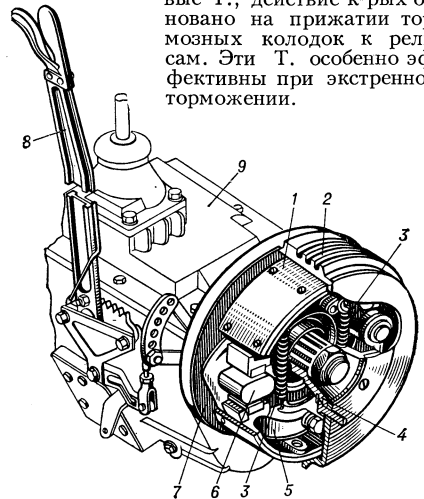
Трансмиссионный тормоз автомобиля: 1 — тормозная накладка; 2 — тормозной барабан; 3 — стяжная пружина; 4 — фланец вторичного вала коробки передач; 5 — колодка; 6 — разжимной кулак; 7 — тормозной щит; 8 — рычаг привода ручного тормоза; 9 — коробка передач.
